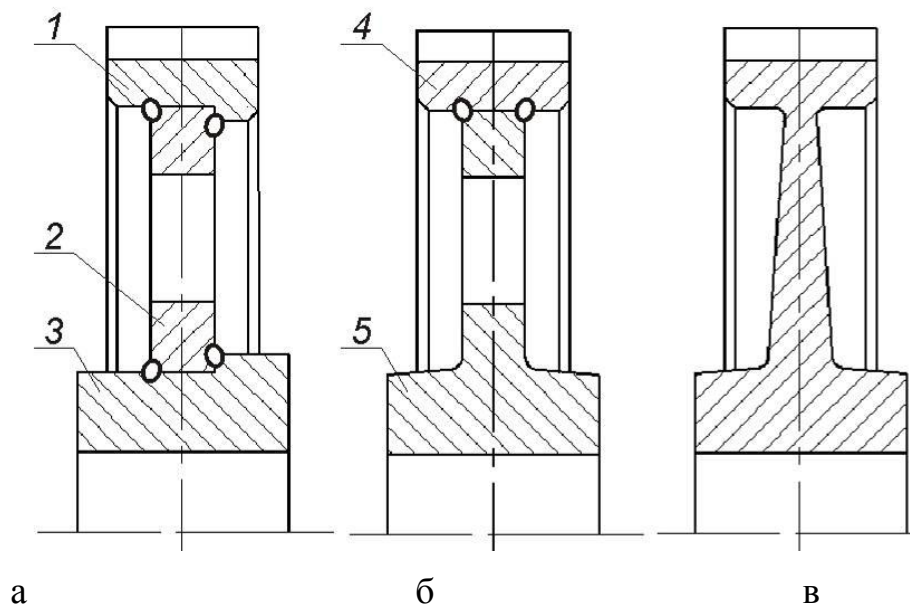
Конструктивні варіанти заготовки шестерні:
